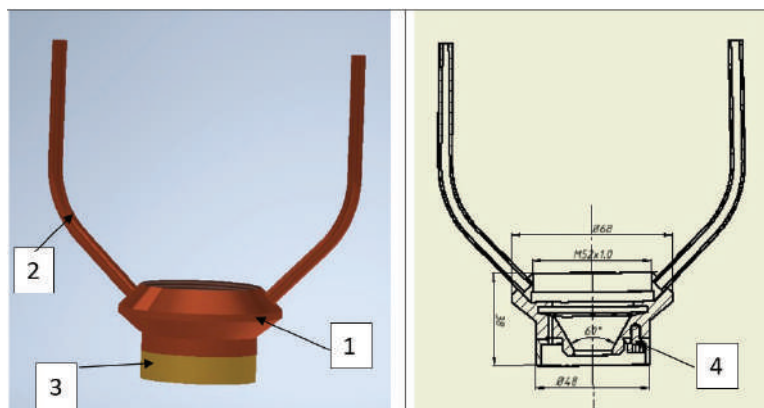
Загальний вигляд та поперечний розріз сопла для подачі захисного газу: 1 – сопло захисного газу; 2 – трубки подачі порошку; 3 – ковпак захисний; 4 – гвинт фіксації захисного ковпака
